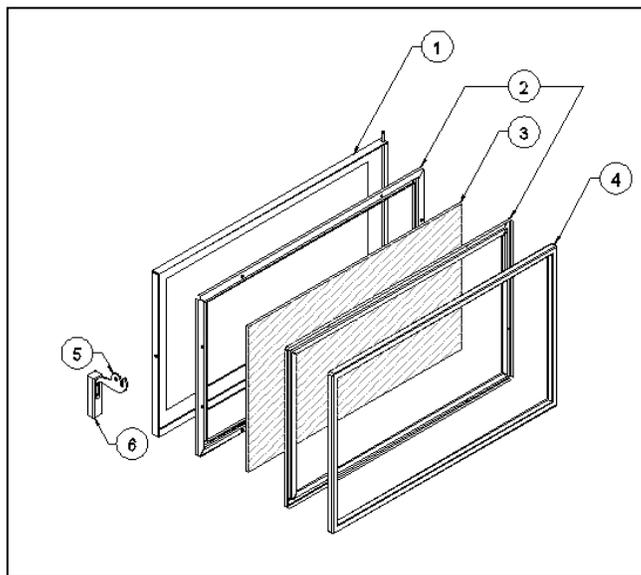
Vue Explosée de l'Assemblage de la Porte
